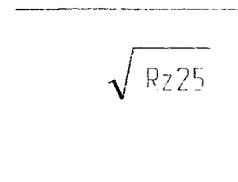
Указание шероховатости, одинаковой одинаковой для всех поверхностей детали
